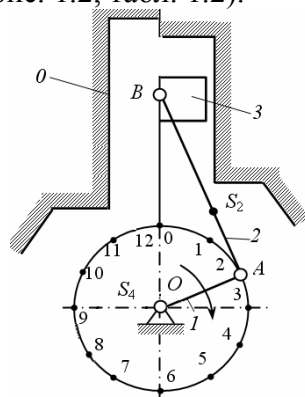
Схема механізму поршневого двигателя аеродромного газозаправника
